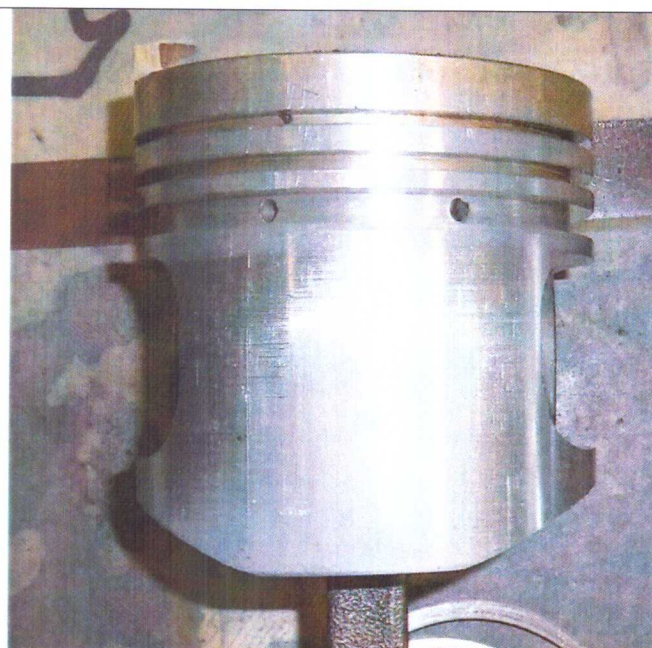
Внешний вид боковой поверхности поршня первого цилиндра по окончании длительных испытаний двигателя при работе на базовом масле Castrol EDGE с добавкой нанокompозита Amortect PROOF
